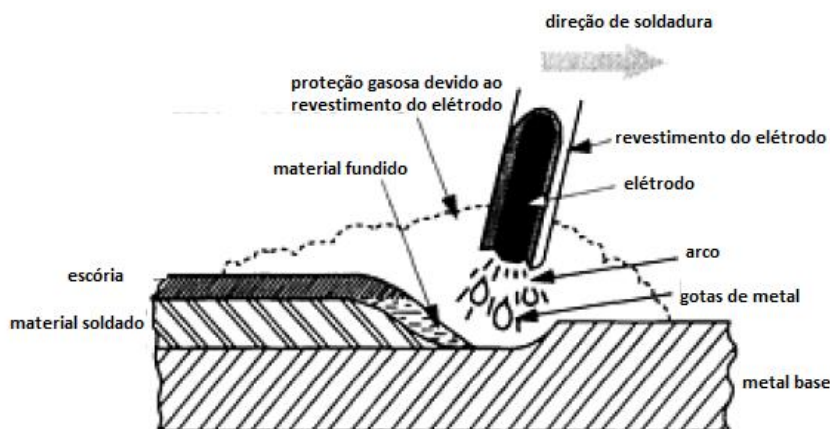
esquema ilustrativo do processo de soldadura de eléctrodo revestido [7]
